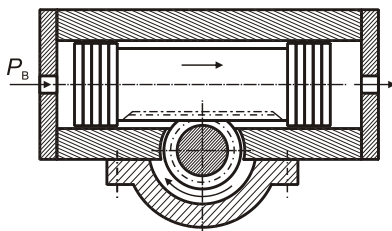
Поворотный пневмоцилиндр ($P_{в}$ — давление воздуха)
